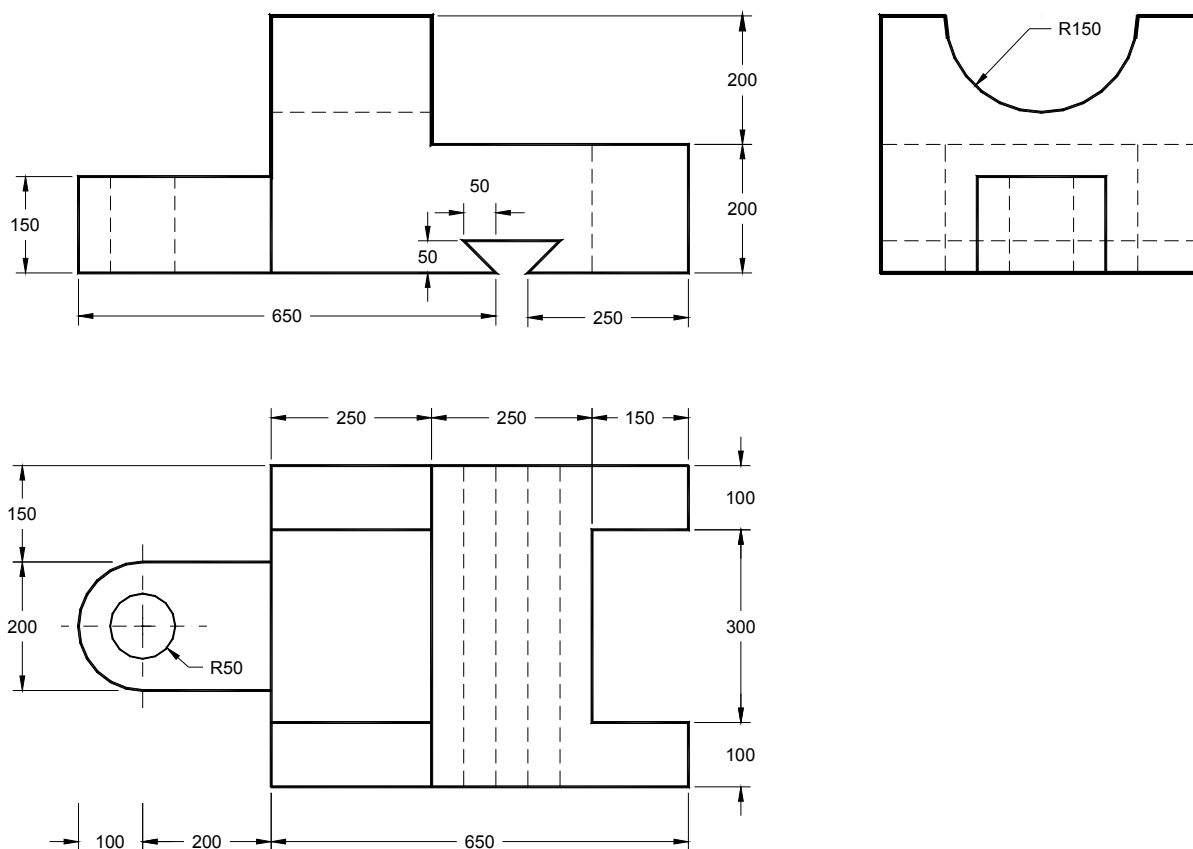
Projeto do objeto utilizado para teste de corte
